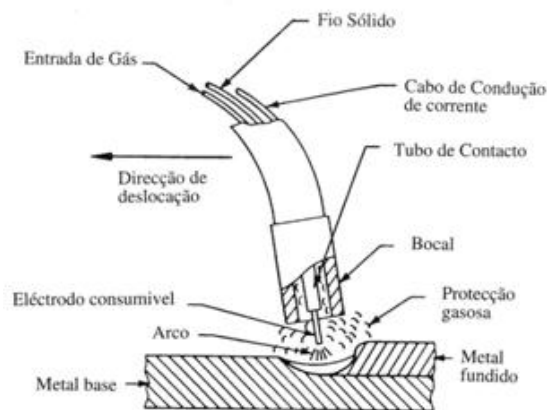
Esquema de soldadura MIG/MAG [6]
